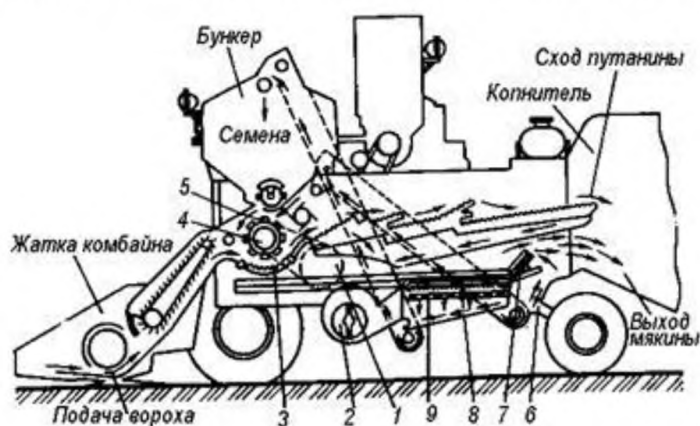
Зернозбиральний комбайн для переробки льняного вороху: 1 - шків контрприводу; 2 - заслінка вентилятора; 3 – дека молотильного відділення; 4 -шків барабана; 5 - бич барабана; 6-щиток колосового шнека; 7 - подовжувач верхнього решета; 8 – верхнє решето; 9 - нижнє змінне решето.
